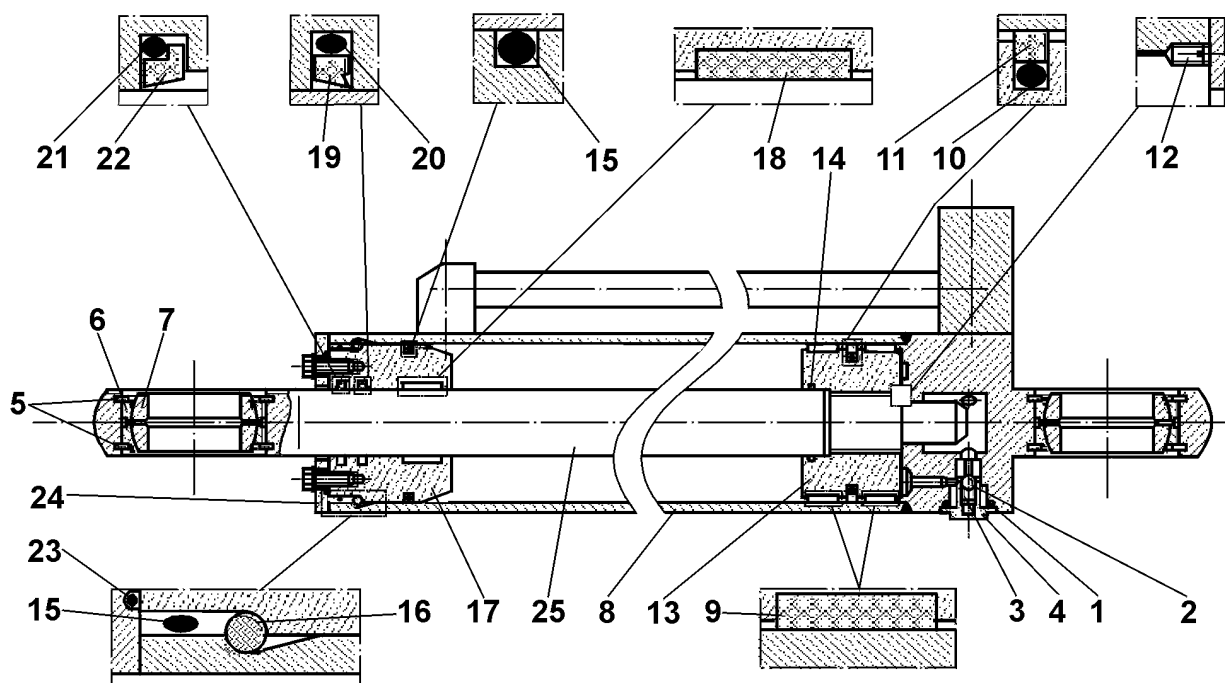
С.4. Гидроцилиндр поворота (разрез)
